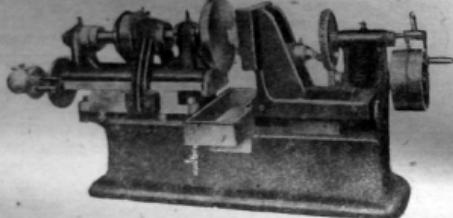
Станок для шлифовки и полировки торцовочных камней.
